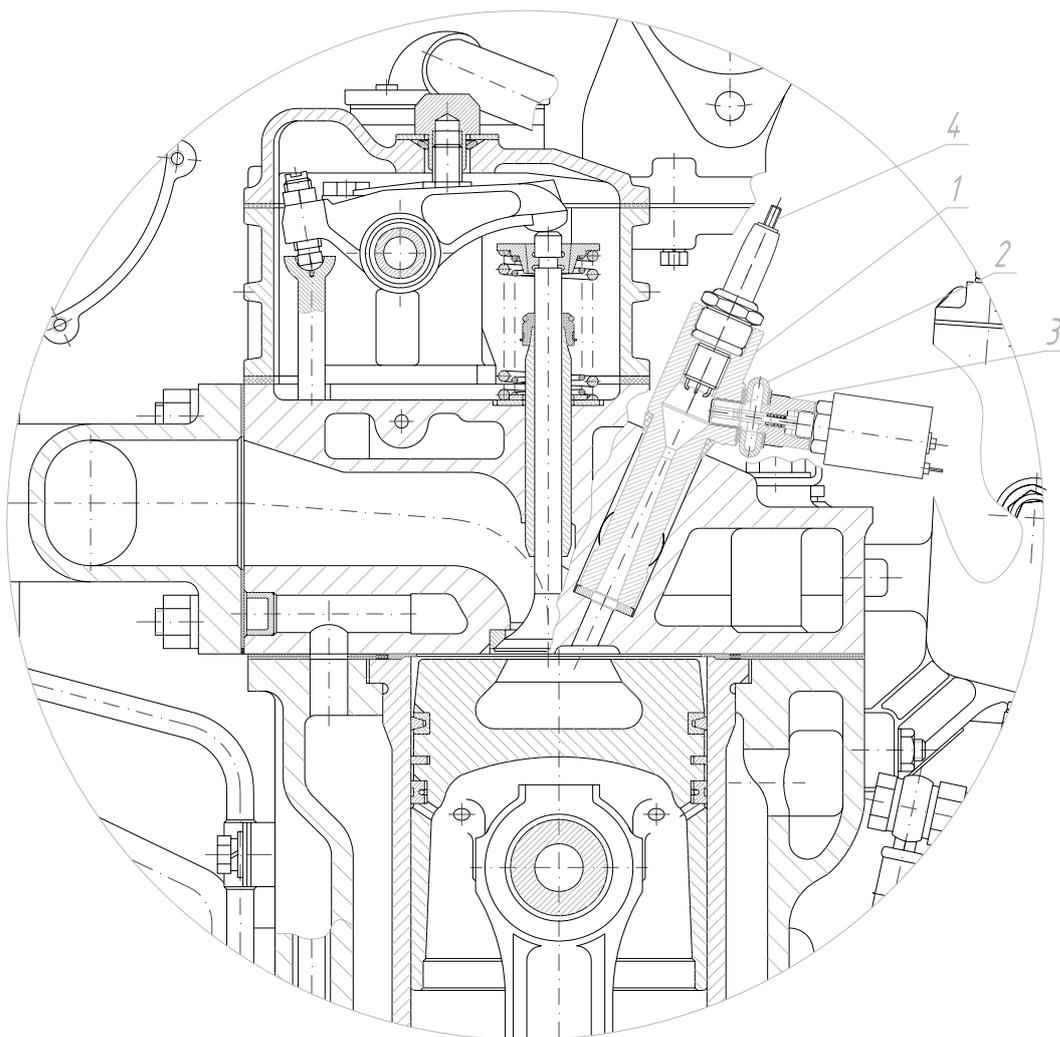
Схема технологии конвертации дизеля Д-240 в газовый с искровым форкамерно-факельным зажиганием: 1- корпус форкамеры; 2- магистраль подвода газа; 3- газовый впускной клапан с электромагнитным приводом; 4- искровая свеча зажигания.
